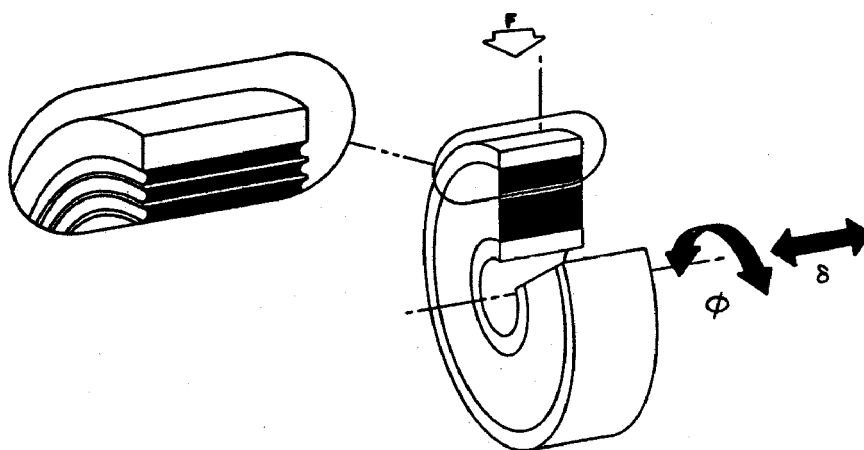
Схема нагружения цилиндрического радиального подшипника
